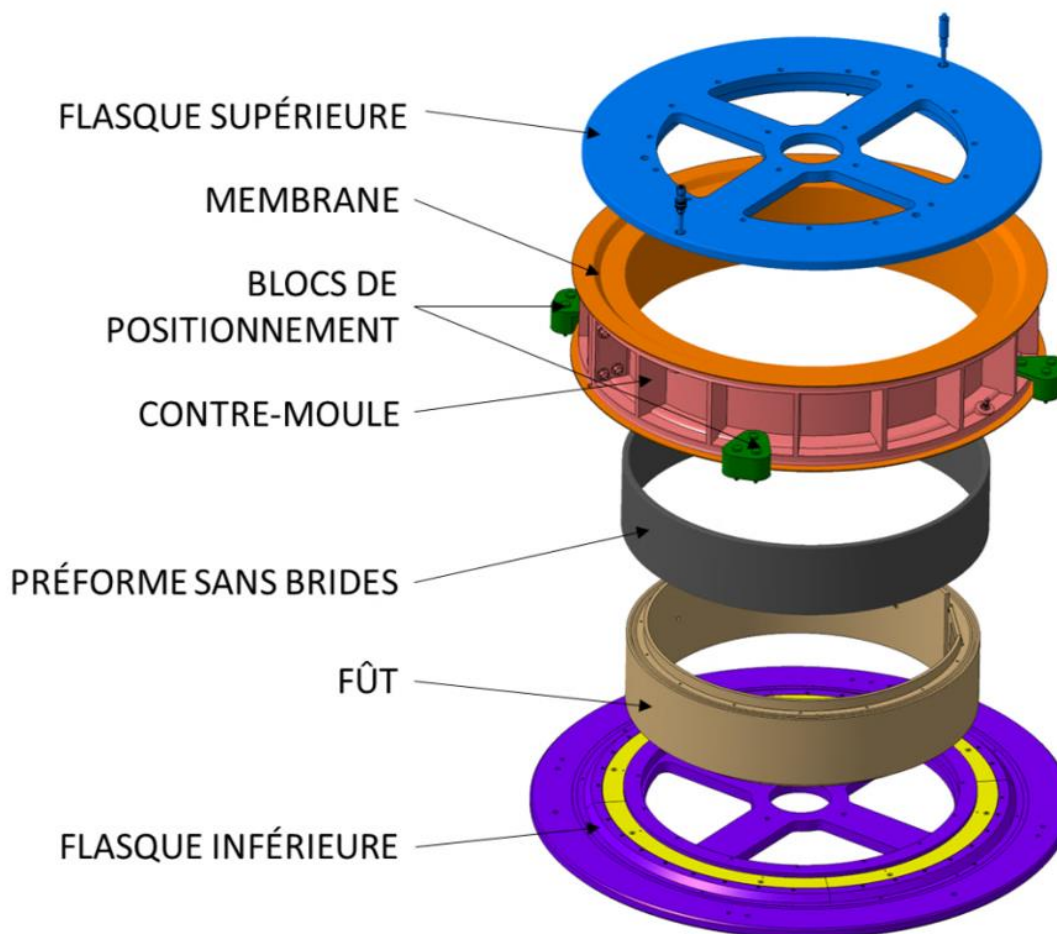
Vue éclatée du moule carter à demi échelle.
